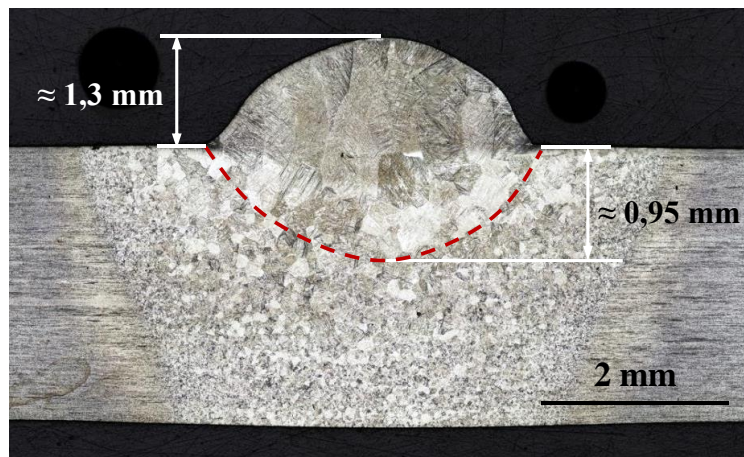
Auftragschweißung im Querschliff, VC-geimpft
